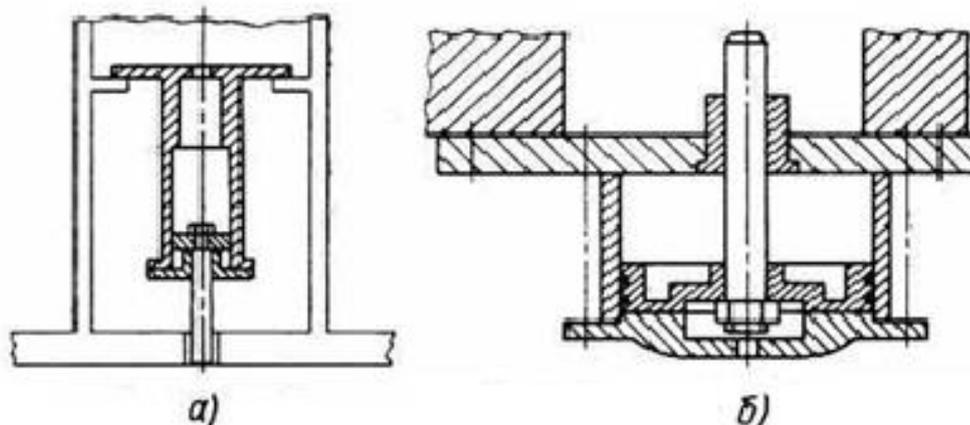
Схема привода выталкивателей от пневмоцилиндра:
